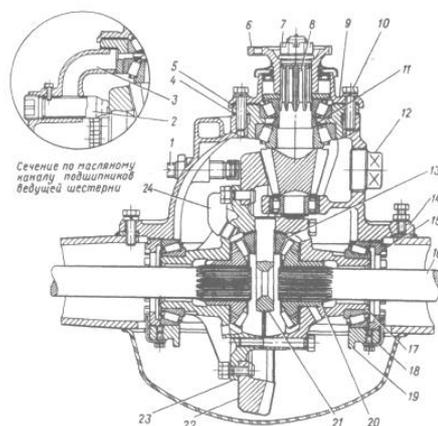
Главная передача:1 — винт упора; 2 — маслоприемная трубка; 3 - верхний канал; 4 — регулировочные прокладки; 5 — муфта подшипников; 6 — фланец; 7 — гайка; 8 — ведущая шестерня; 9 — крышка; 10 — болт; 11 — регулировочное кольцо; 12 — пробка заливного отверстия; 13 — сателлит; 14 — картер; 15 — гайка; 16 — полуось; 17 — правая коробка дифференциала; 18 — стопорная пластина; 19 — крышка; 20 — полуосевая шестерня; 21 — крестовина; 22 — ведомая шестерня; 23 — левая коробка дифференциала; 24 — маслоулавливатель.
